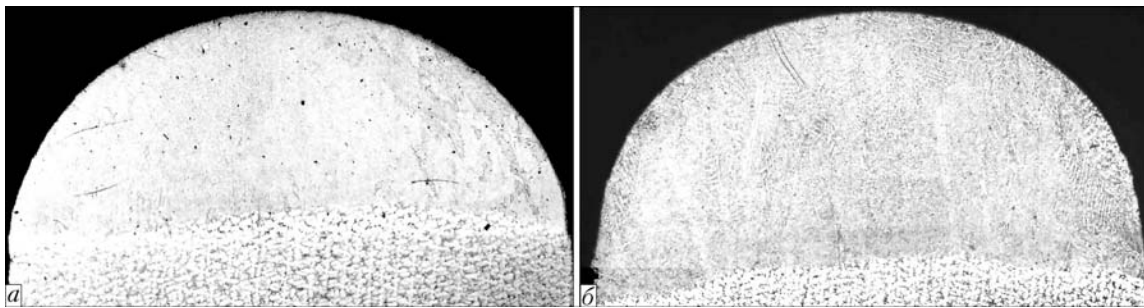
Макрошлифы ($\times 15$) двух- (*a*) и трехпроходной (*б*) наплавки на торец пластины, направление наплавки [013], плоскость наплавки (100), плоскость шлифа (031)
